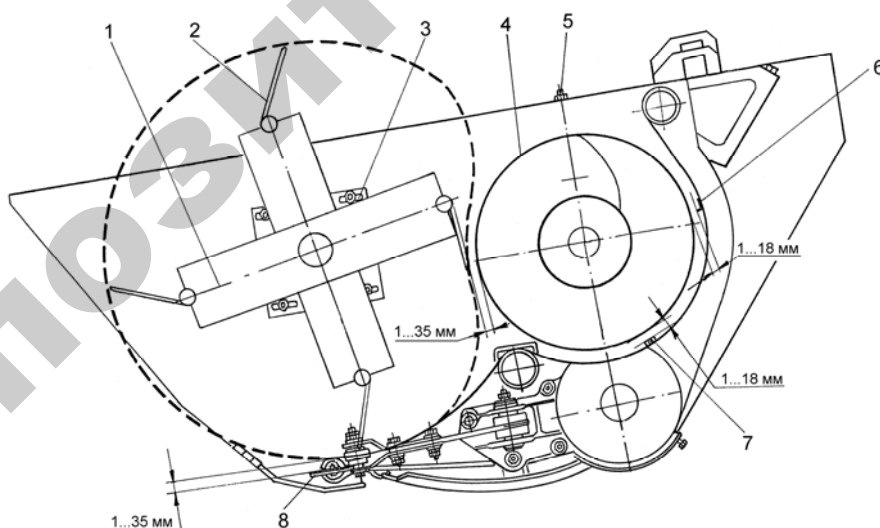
Регулировка положения мотовила и шнека жатки для трав:
